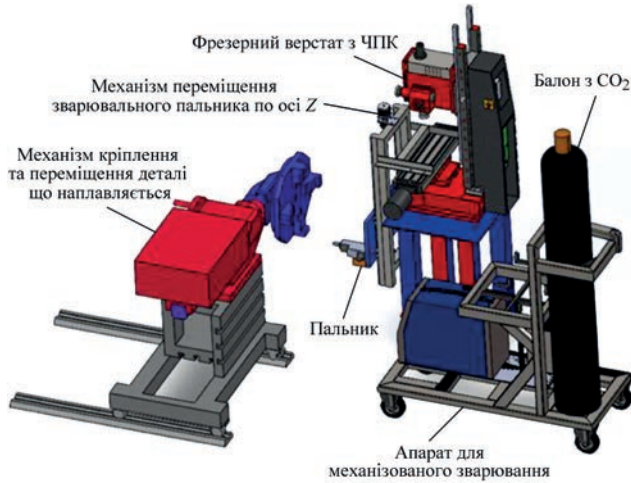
Схема 4-координатної установки для адитивного наплавлення способом MAG
